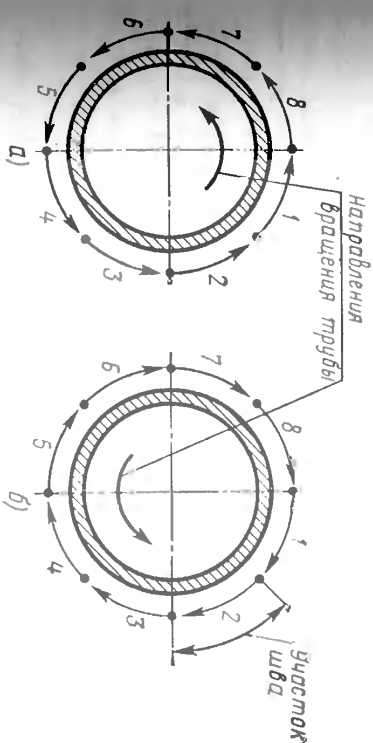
Схема сварки стыков труб большого диаметра: а, б — наложение соответственно первого и второго слоев
